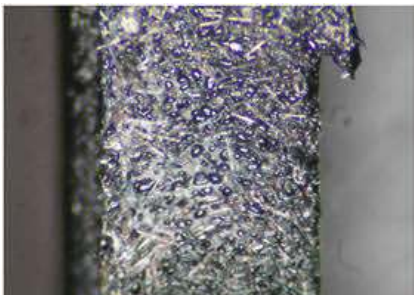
Unter dem Mikroskop zeigen sich Blasen in der Schweißnaht, die bei einem zu hohen Wassergehalt im geschweißten Kunststoff auftreten
